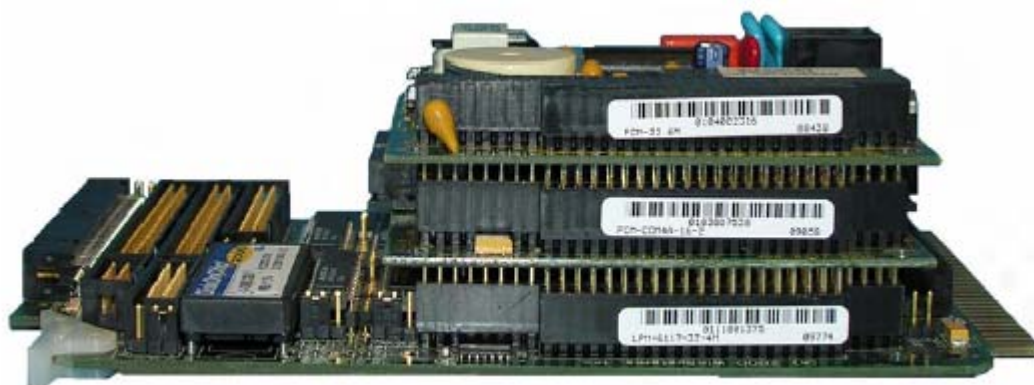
Сборка каркаса для печатных плат Модели 700
